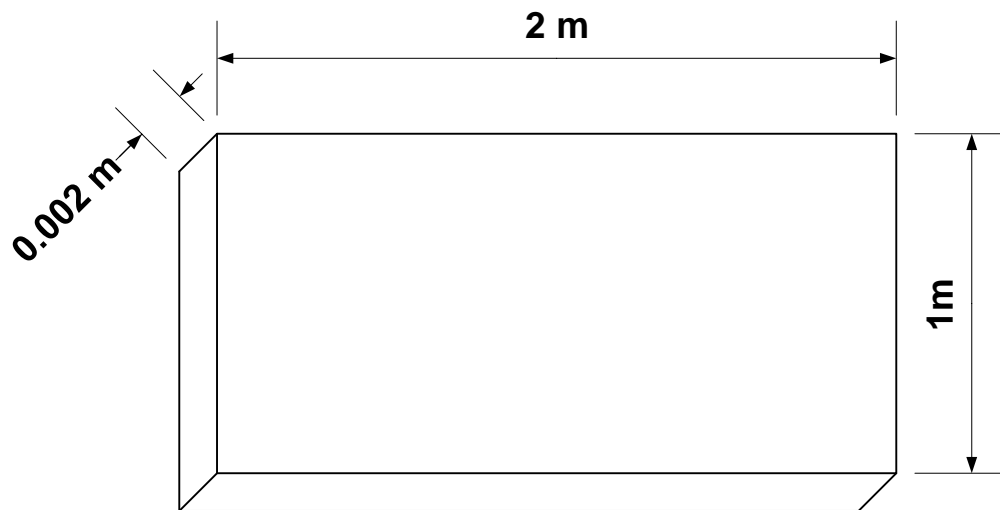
Dimensions des chaque couches unidirectionnelles.
